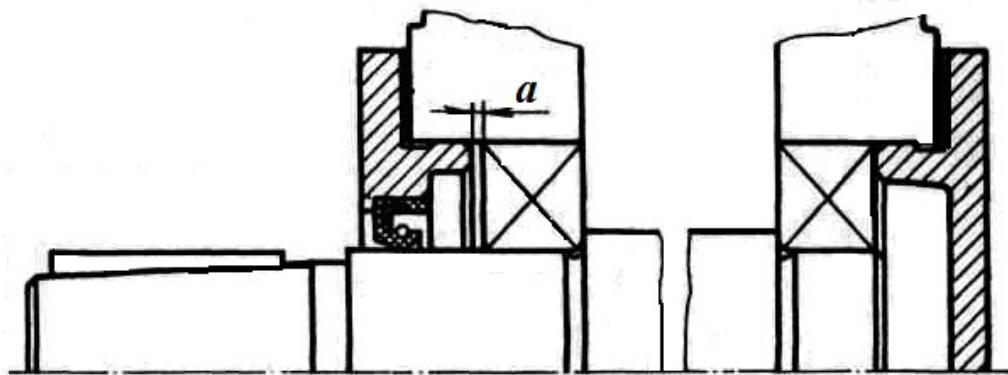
Установка радиальных подшипников, закрытых привертными крышками
